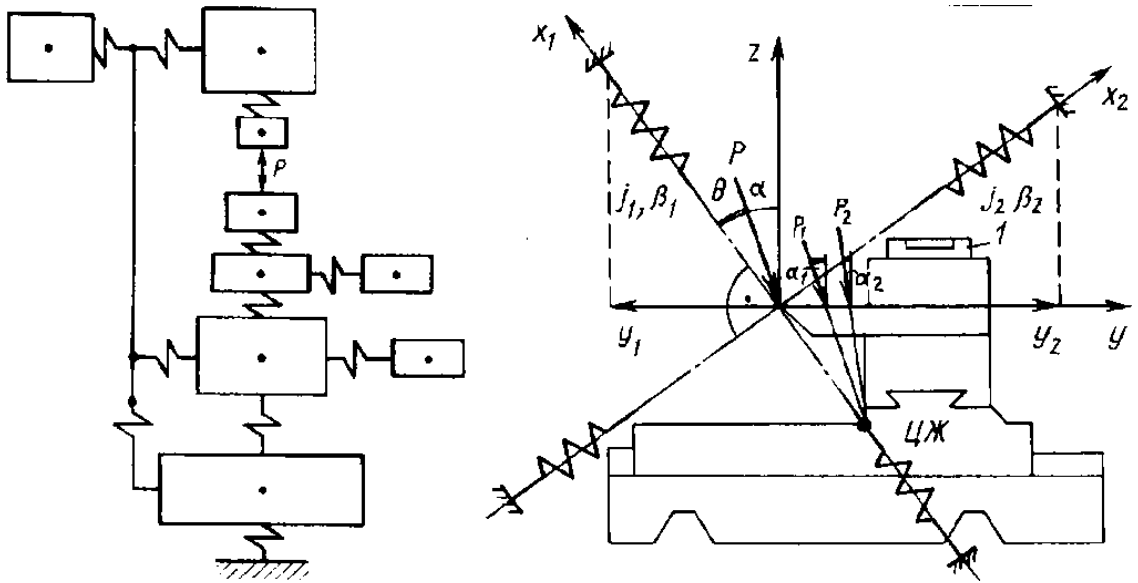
Расчетные схемы с доминирующей колебательной системой элементов металлорежущего станка [54, 88]
